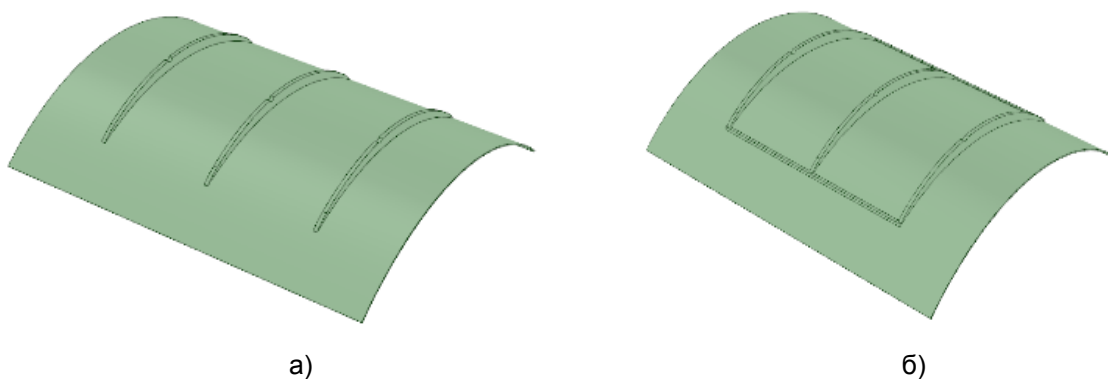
Смазочный слой для колодки №3- с тангенциальными щелевыми соплами:
